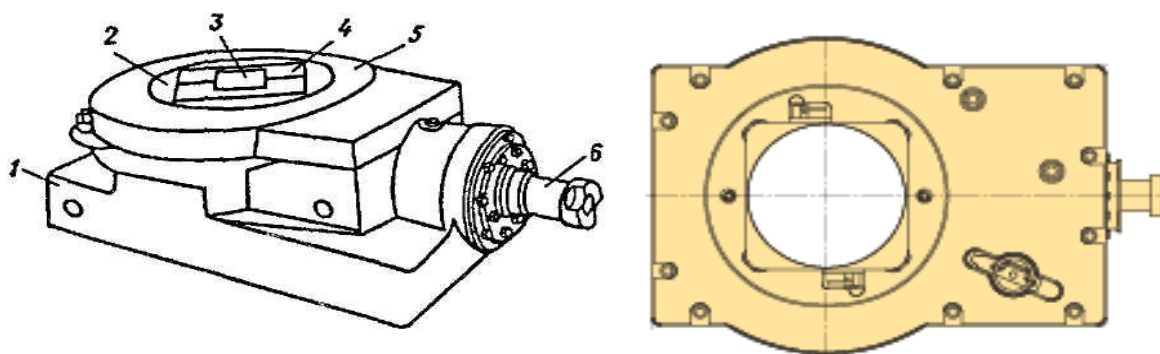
Ротор Р-1260 и его станина (справа): 1 - станина; 2 - стол с укрепленным зубчатым венцом; 3 - зажимы; 4 - вкладыши; 5 - кожух; 6 - вал
